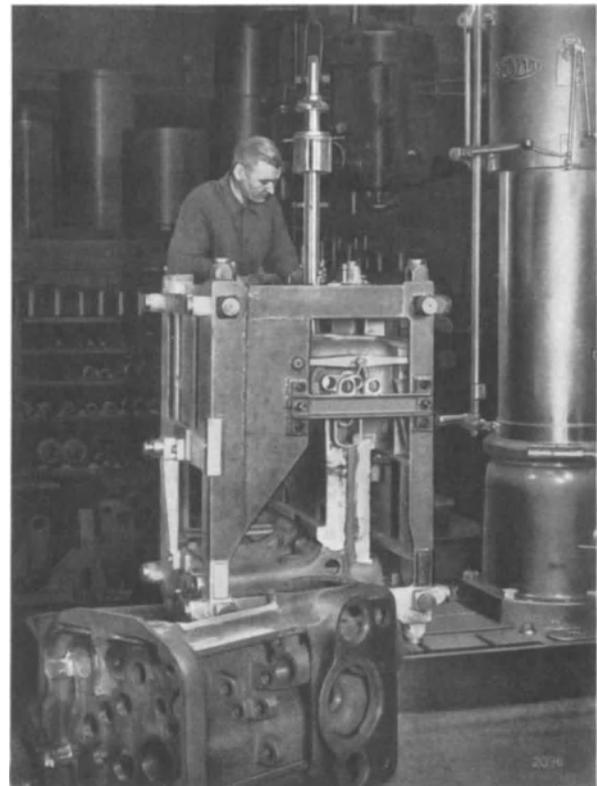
Einfädeln einer Bohrstange in die Vorrichtung mit einem Hebezeug
